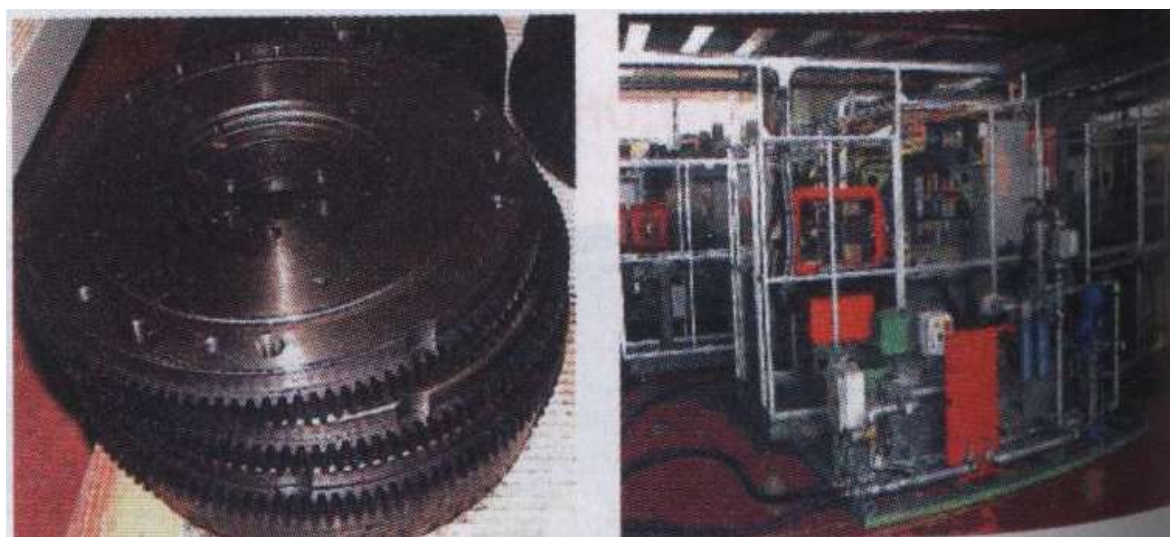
Комплекс для гарту і віджигу венца шестерні коробки передач і її наступною гарячою запресовкою на маховик
